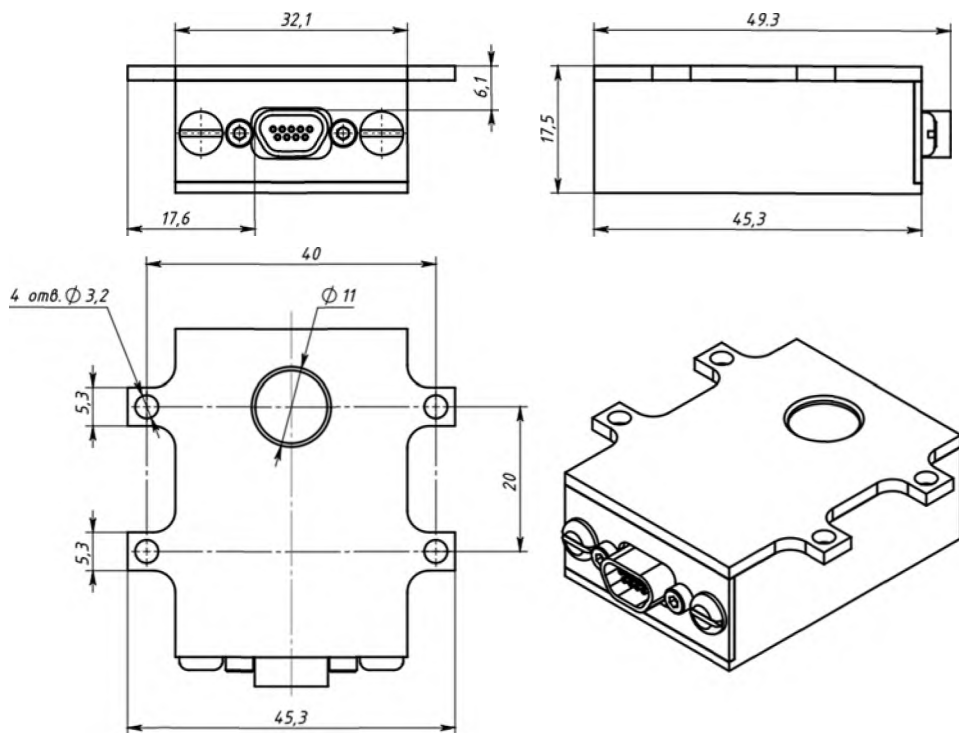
Габаритный чертёж солнечного датчика SX-SUNR-01
